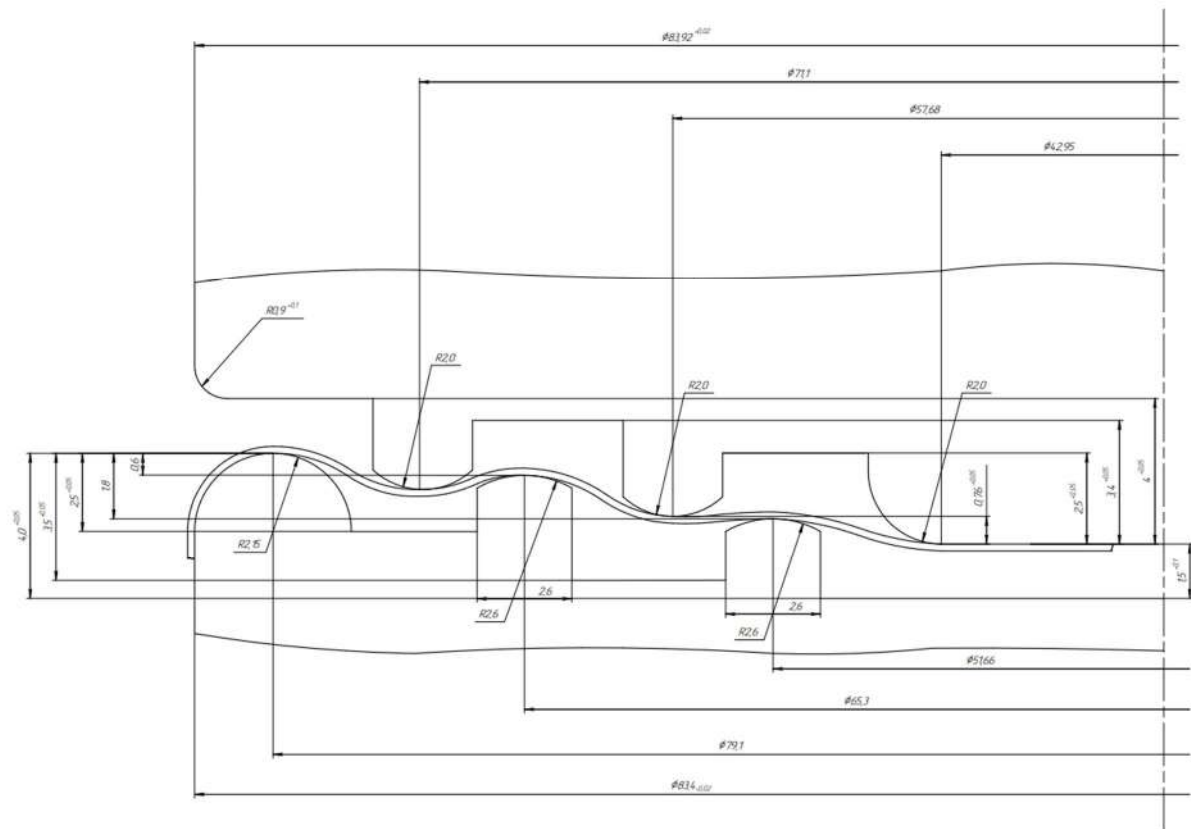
Верхній та нижній рельєфи жерстяної банки №6. Розмірами рис. 16:
